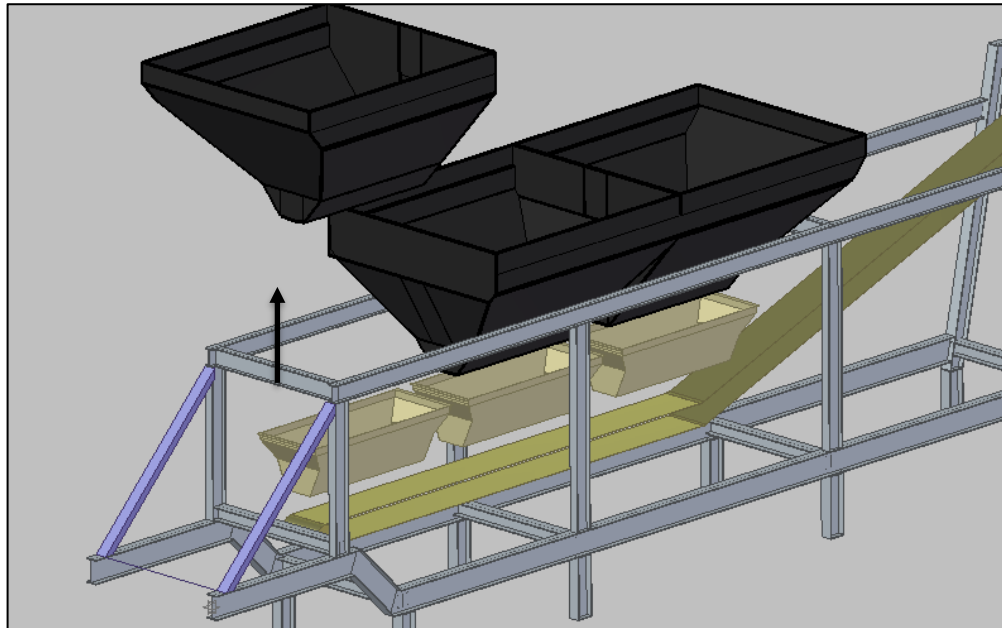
Soldadura de la estructura de la compuerta con la tolva
